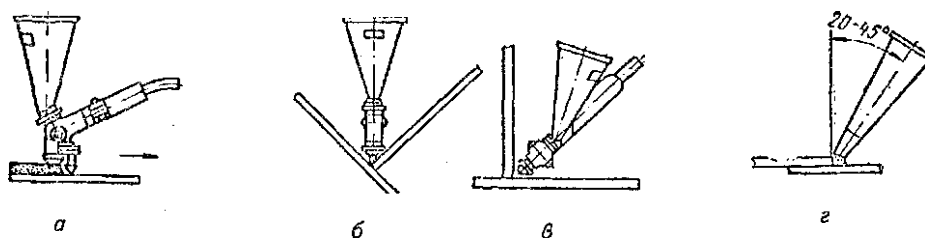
Схема полуавтоматической сварки под флюсом: а — стыковых швов; б — в положении «в лодочку»; в — тавровых швов; г — нахлесточных швов
